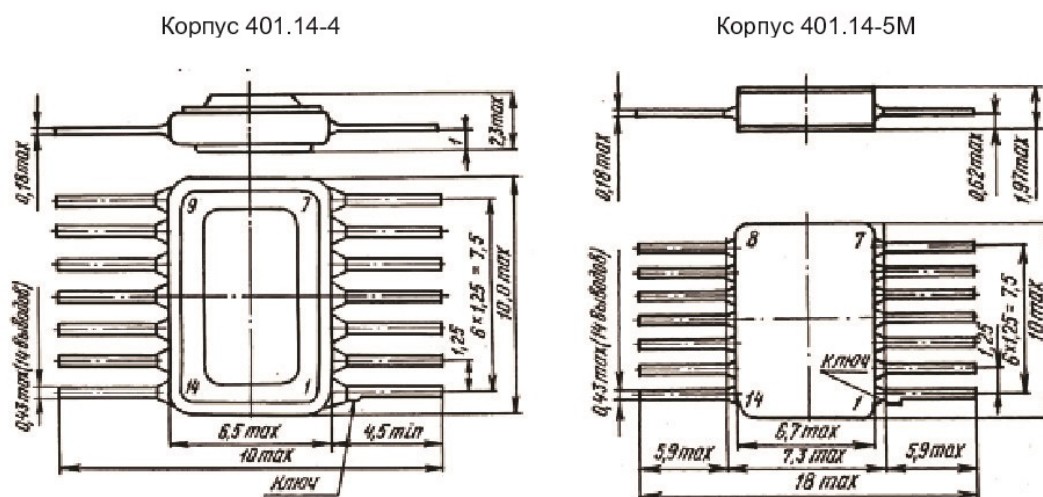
Габаритные чертежи корпусов 401.14-4 и 401.14-5М
